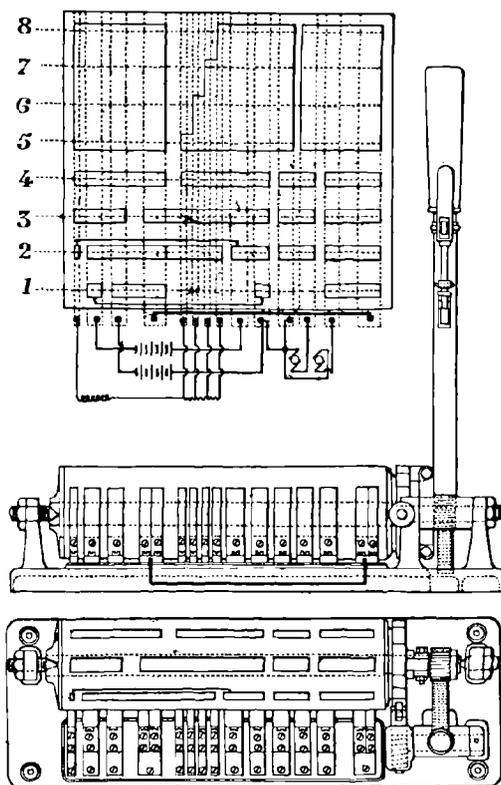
Développement, élévation et plan du combinateur Joël.
